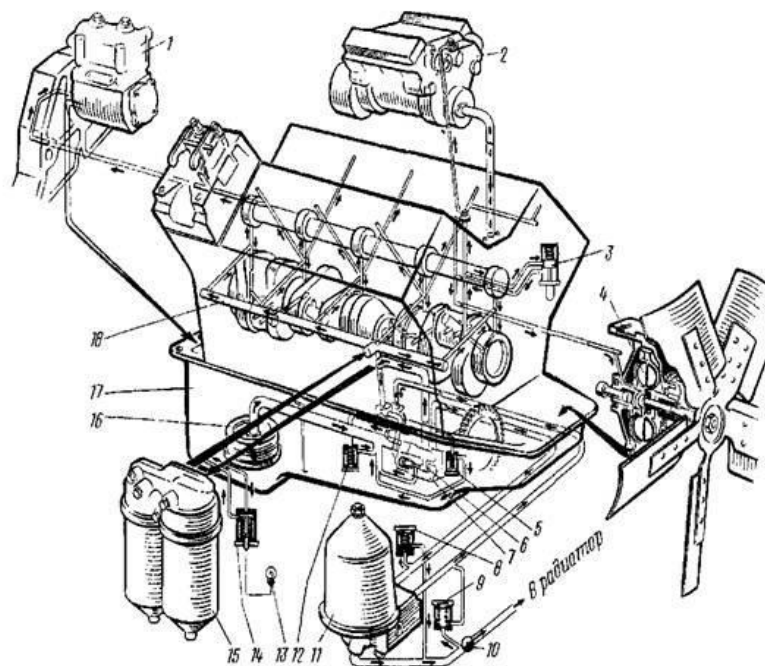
Схема системы смазки 1—компрессор; 2—топливный насос высокого давления; 3—выключатель гидромукты; 4—гидромукта; 5, 12—предохранительные клапаны; 6—клапан системы смазки; 7—насос масляный; 8—перепускной клапан центробежного фильтра; 9—сливной клапан центробежного фильтра; 10—кран включения масляного радиатора; 11—центробежный фильтр; 13—лампа сигнализатора засоренности фильтра очистки масла; 14—перепускной клапан полнопоточного фильтра; 15—полнопроточный фильтр очистки масла; 16—маслоприемник; 17—картер; 18—главная магистраль
